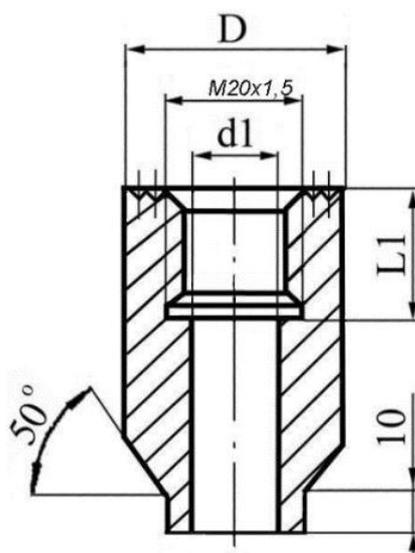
Закладная конструкция для крепления к трубопроводу
